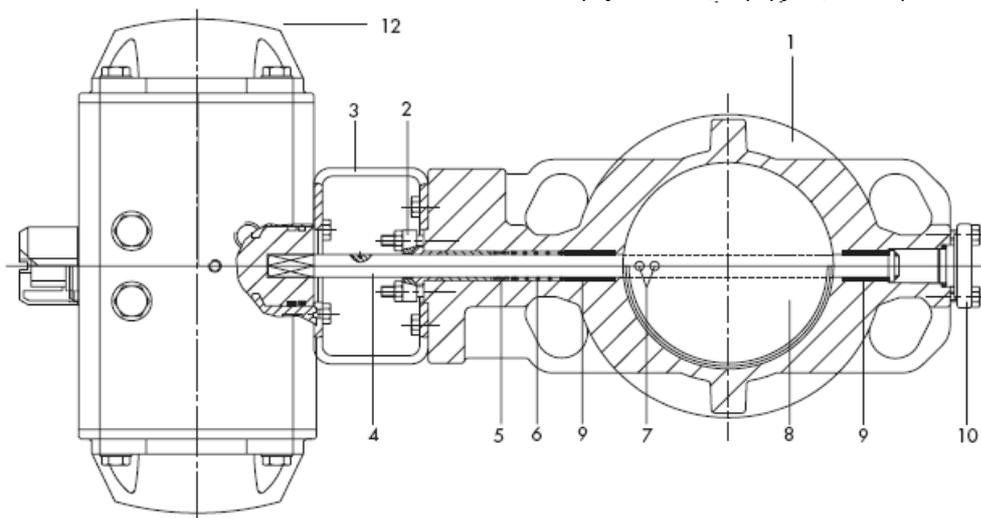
• Пневматическая регулирующая заслонка Тип 3331 / BR 31a
